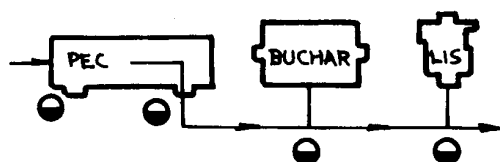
Umístění pece a bucharu ve stejné úrovni
